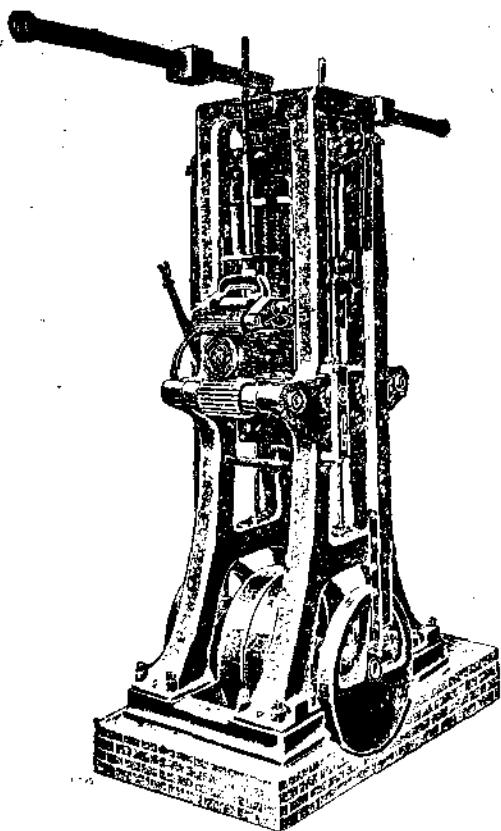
Рамный лесопильный станок для распиловки коротких кряжей.
